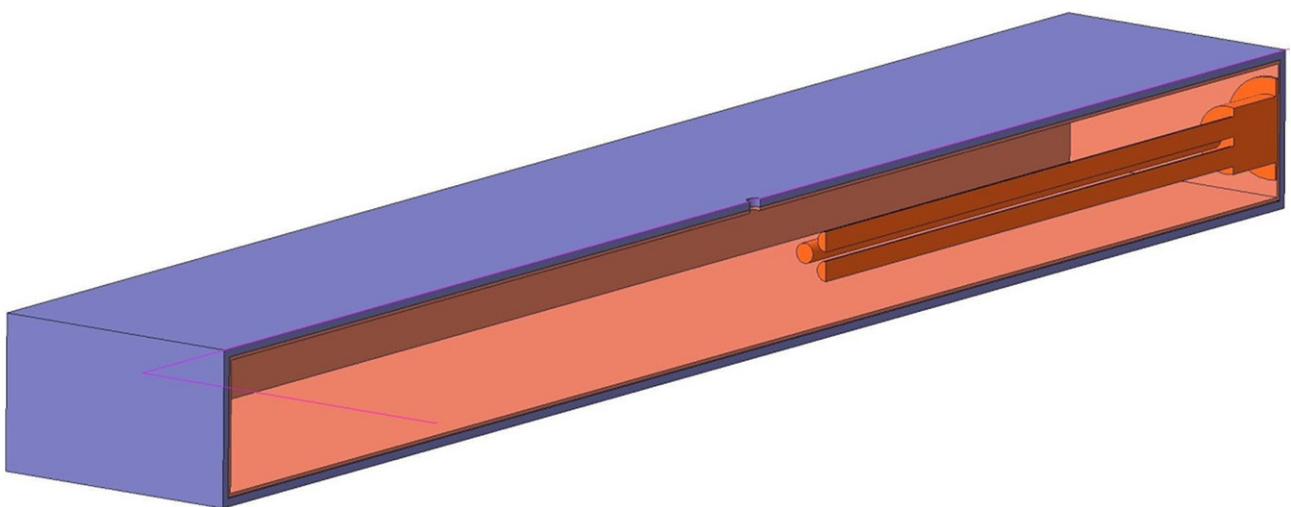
3D-модель сливного резервуара с установленным погружным нагревателем (в разрезе)
